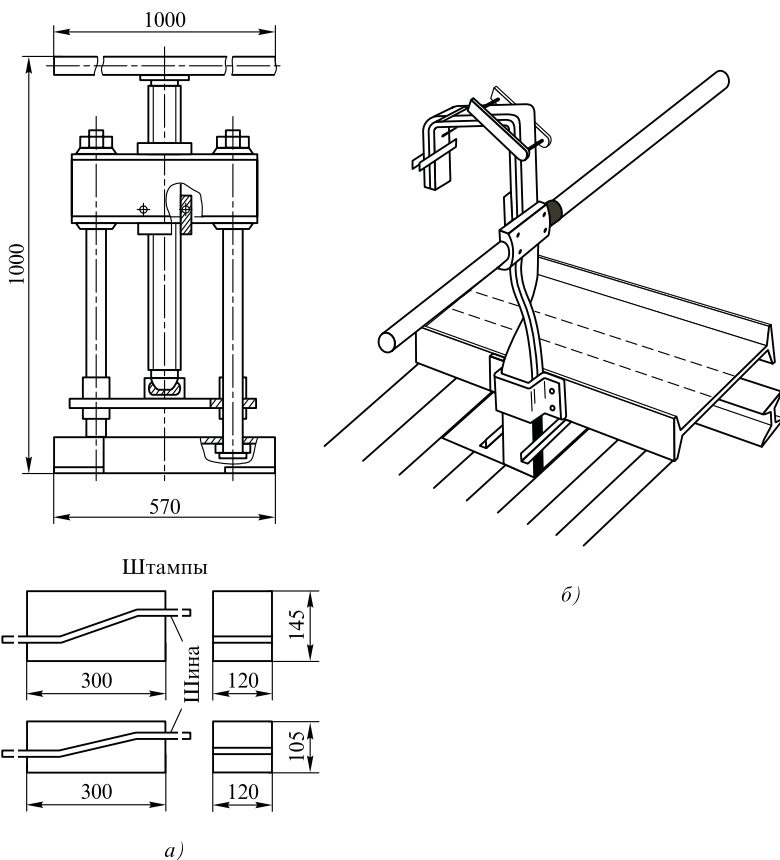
Пресс и штампы для изгиба шин «уткой» (а) и приспособления для изгиба шин «штопором» (б)
